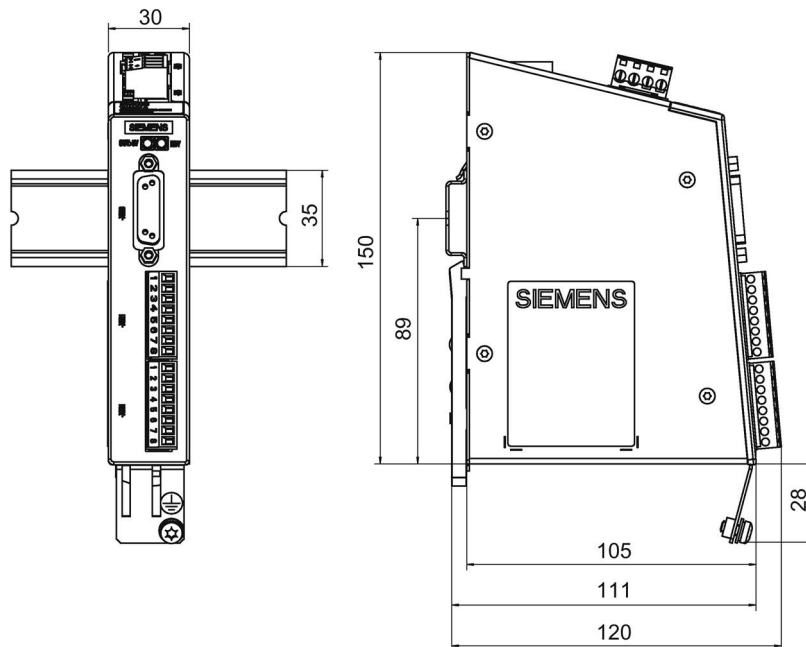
Габаритный чертеж сенсорного модуля SMC30
